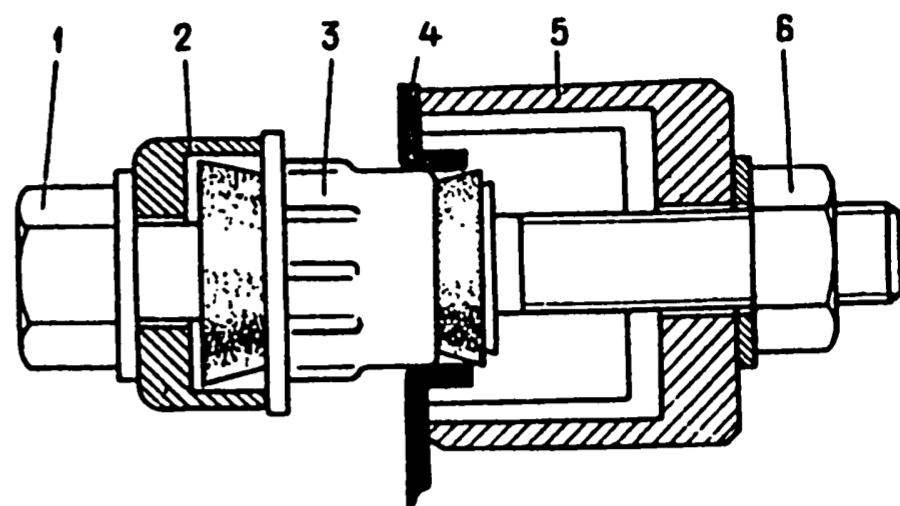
Схема запрессовки шарнира верхнего рычага: 1 - болт; 2 - кольцо приспособления А.47046; 3 - шарнир; 4 - верхний рычаг; 5 - стакан приспособления А.47046; 6 - гайка
